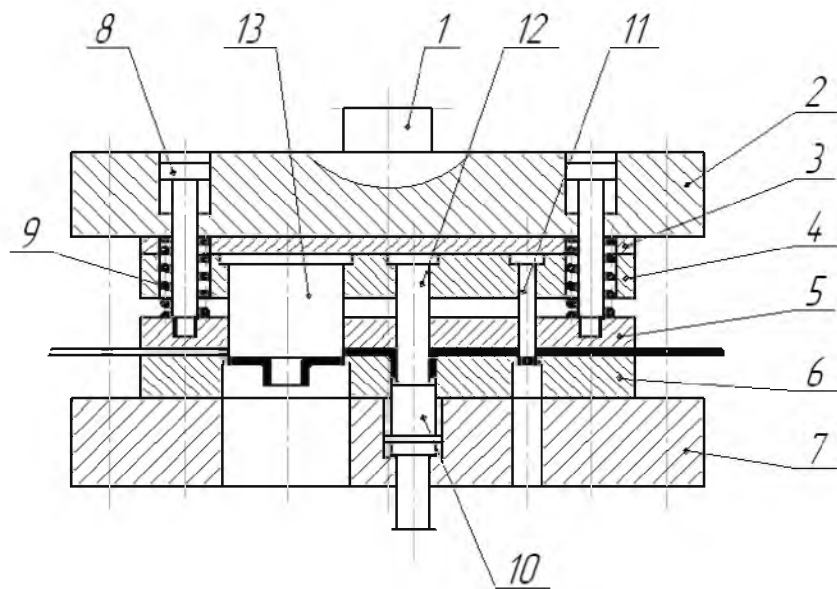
Схема штампа последовательного действия для пробивки, отбортовки и вырубки
